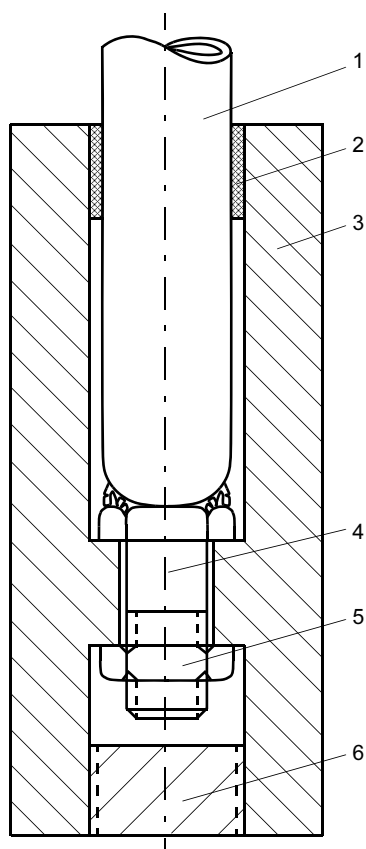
Устройство защиты чехла термопары: 1 — чехол термопары; 2 — герметизирующая замазка (шамотный порошок на жидком стекле); 4 — болт (приварен к чехлу); 5 — гайка для крепления графитового стержня (3); 6 — графитовая резьбовая заглушка
